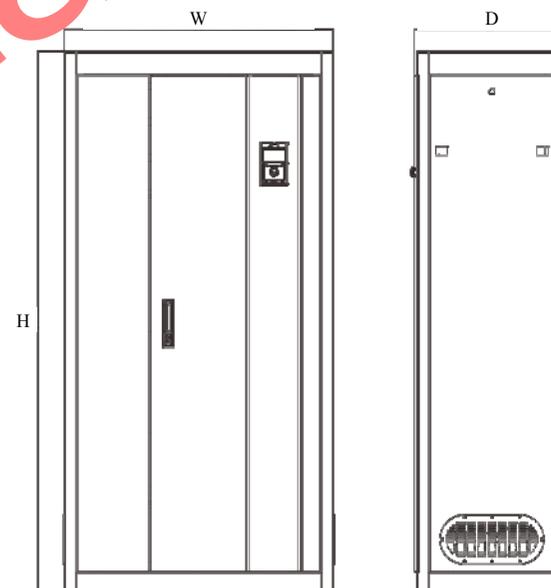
Внешний вид шкафов типоразмеров 12 - 13
